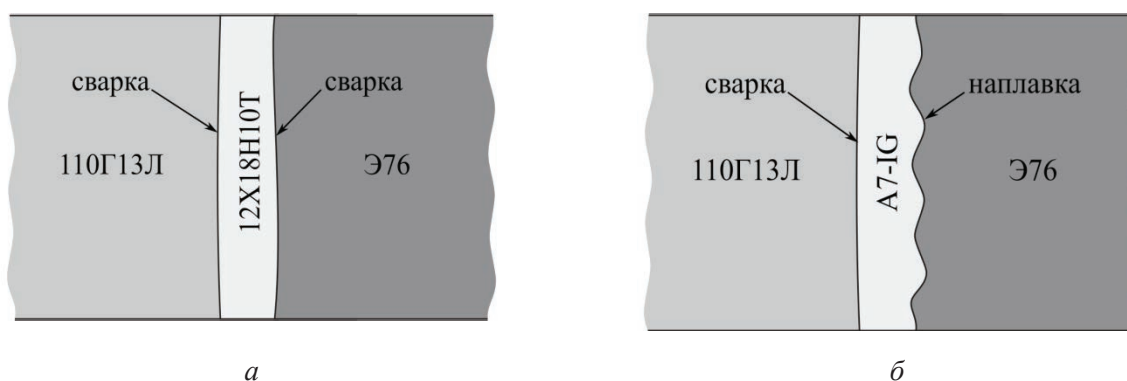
Схема образцов, полученных с использованием технологии стыковой контактной сварки (а) и комбинацией технологий наплавки и стыковой контактной сварки (б)
